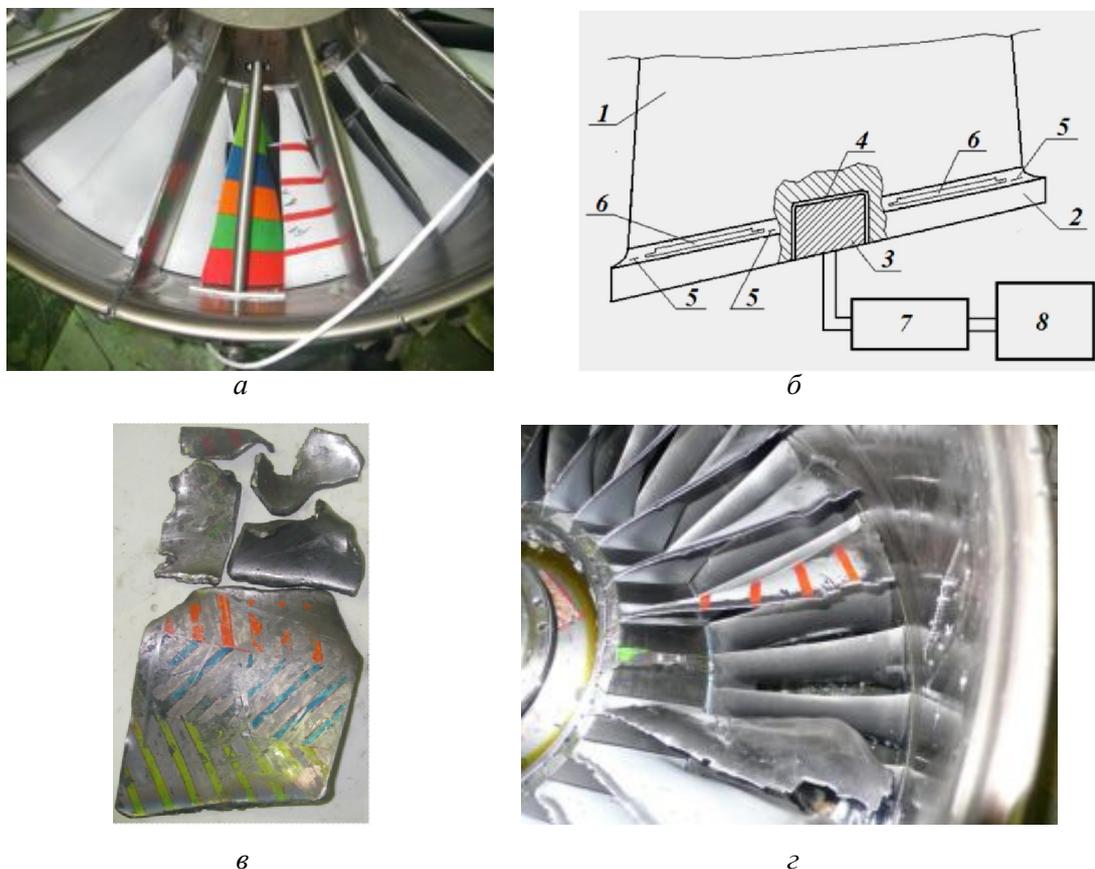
Испытание корпуса вентилятора ГТД на непробиваемость с обрывом лопатки без использования взрыва: а – вентилятор с подготовленной лопаткой; б – схема устройства для обрыва лопатки;
